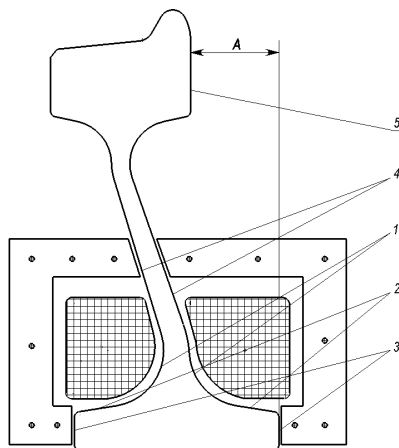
Схема профиля индукционного нагревателя и колеса
